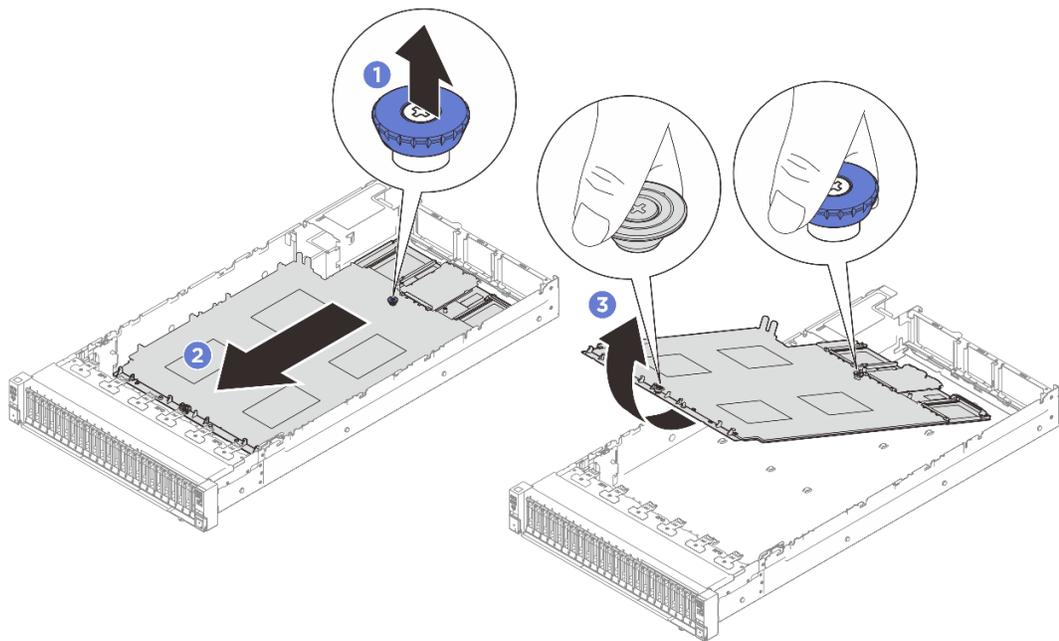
Entfernen der Systemplatinenbaugruppe
